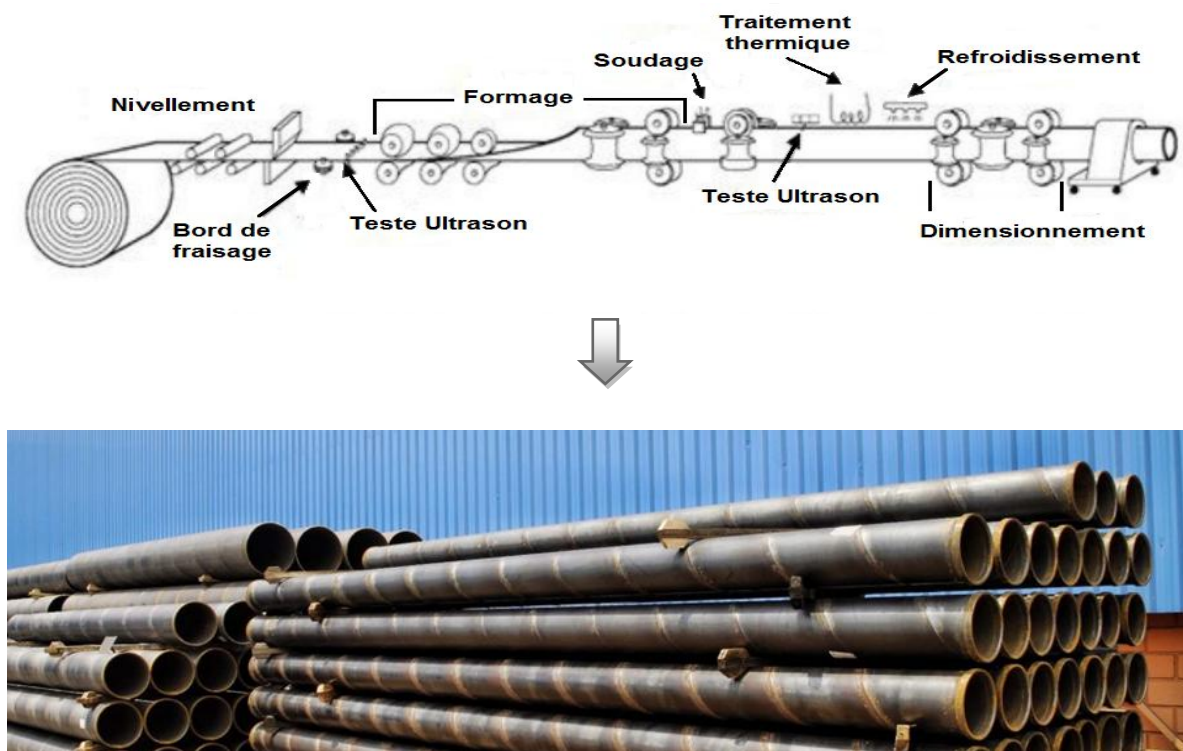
Technique de fabrication des tubes soudés en spirale [ZAZ 17]
